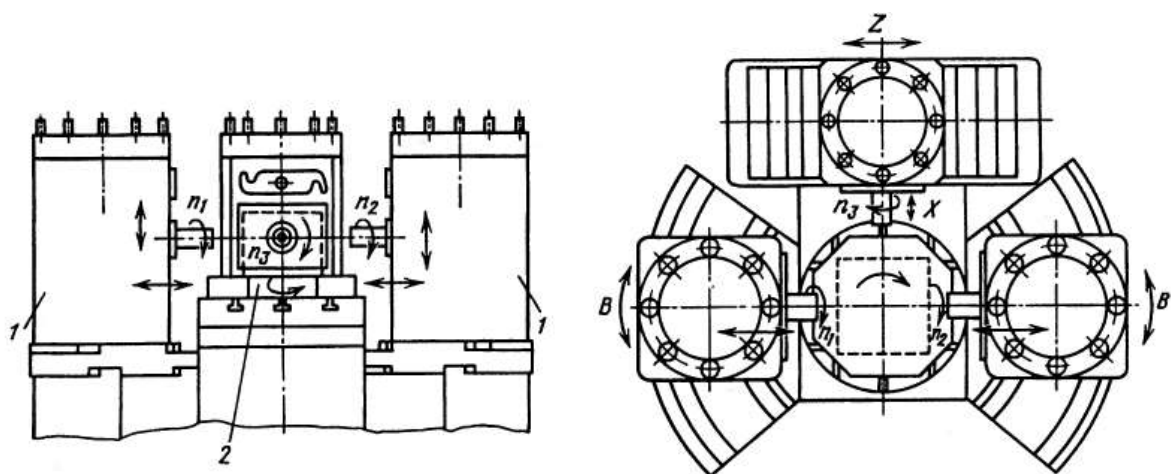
Верстат з ЧПК тристійковий мод. АГП 630-400.
